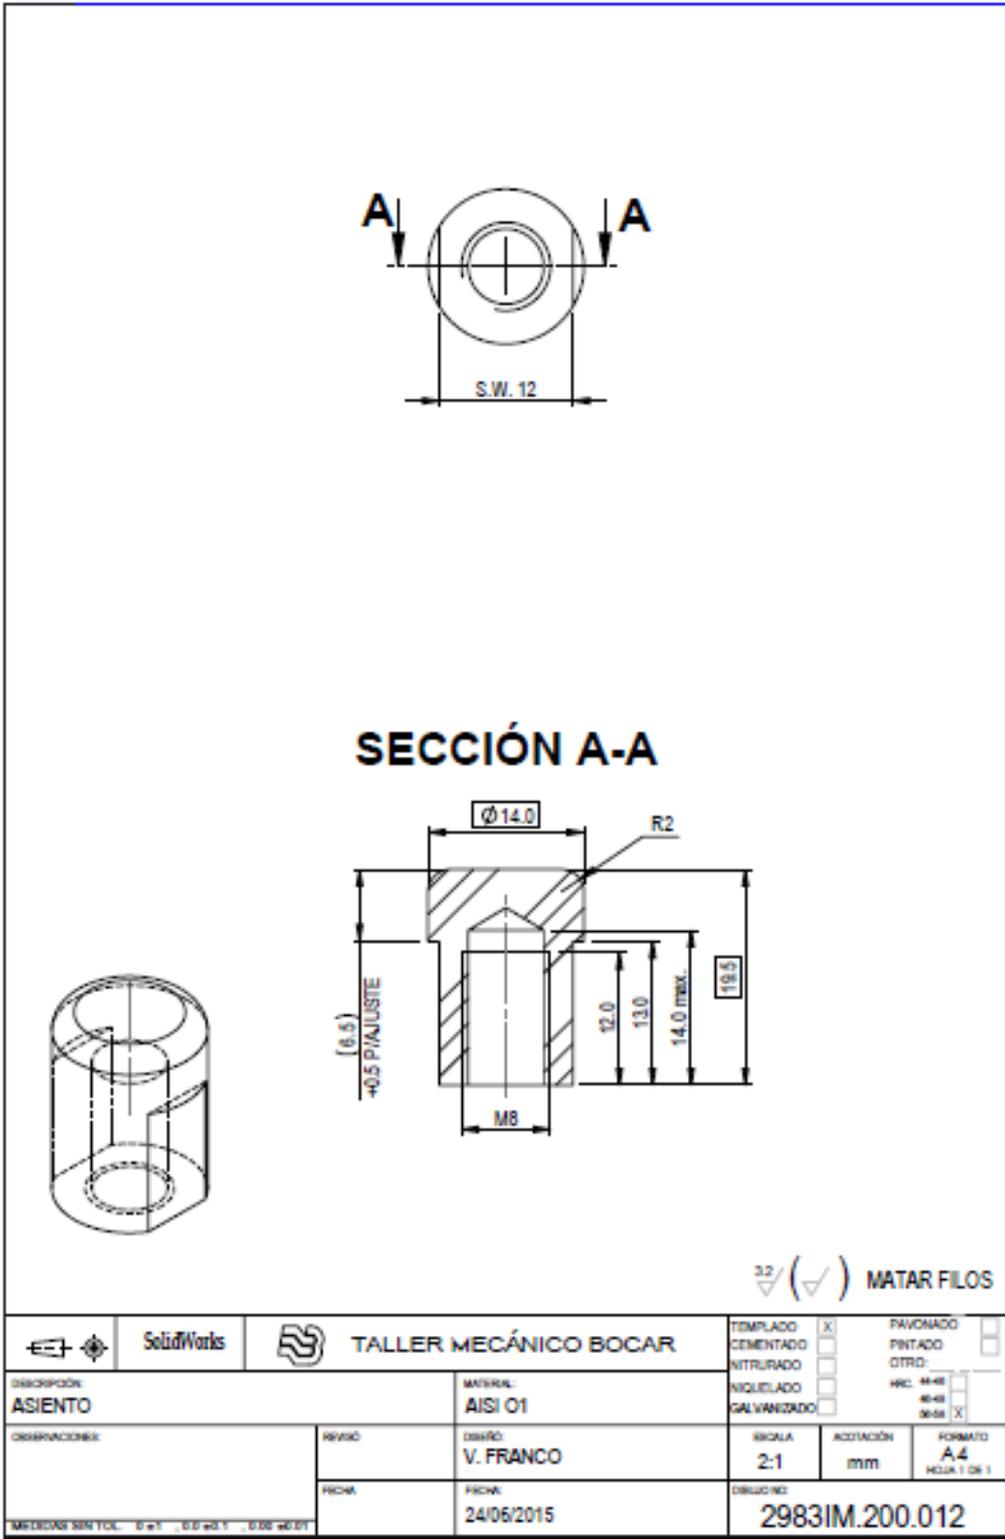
Ilustración VIII-6 Plano de fabricación de asiento para parte inferior.
